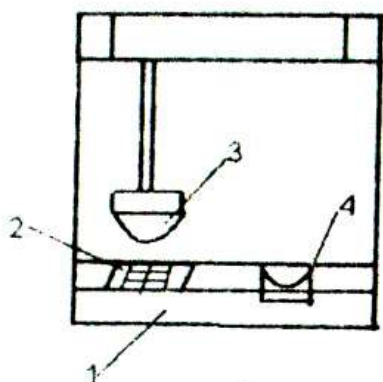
Принципова схема верстату для тамподруку: 1-основа верстату; 2-друкарська форма; 3-тампон; 4-деталь, на яку наноситься зображення
